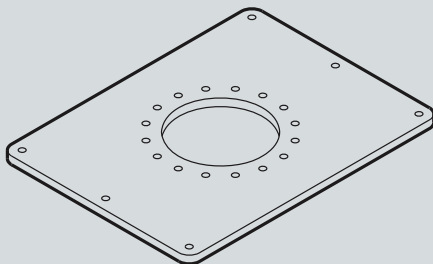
Grundplatte für vertikale Trockenaufstellung
